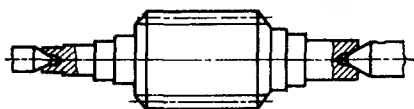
Схема установки червяка при чистовом нарезании витка — нежесткая
